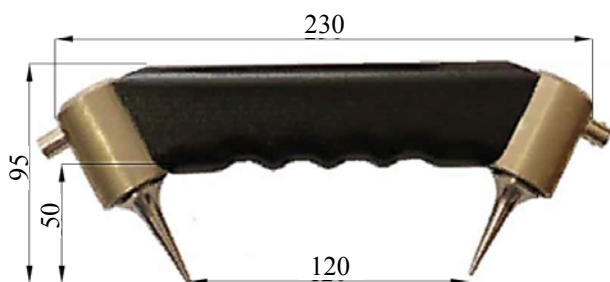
Общий вид измерительной вилки прибора Пульсар 2.1
